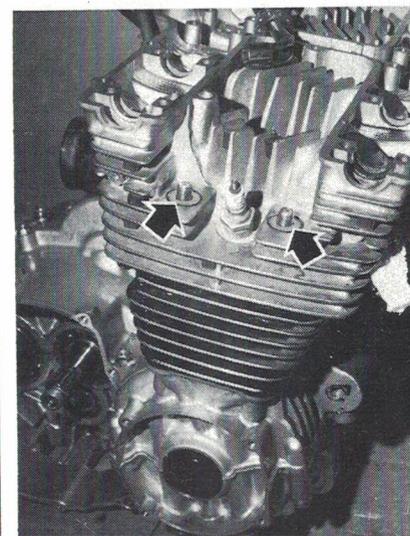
Les deux rondelles cuivre (Photo RMT)
